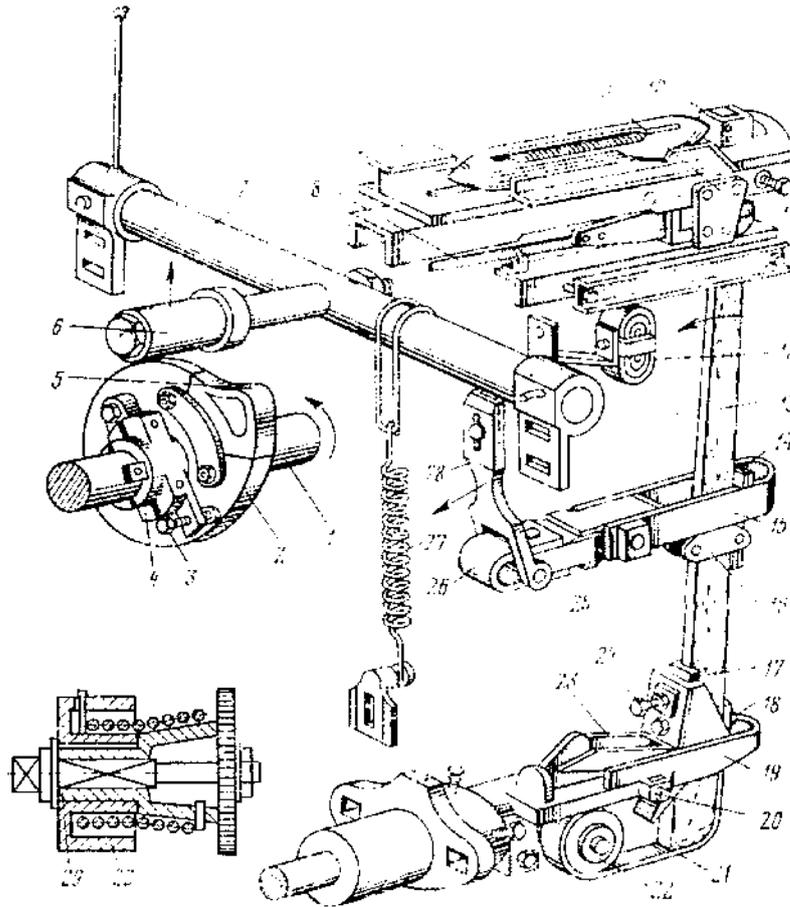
Боевой механизм челючного автоматического станка АТ:
